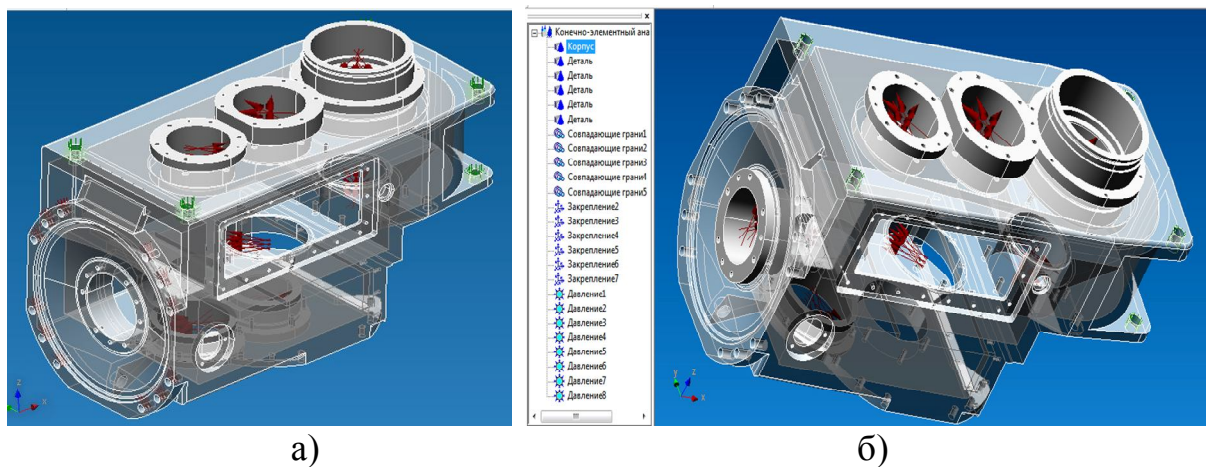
Расчетная модель: а) корпус цилиндрического редуктора, б) корпус коническо-цилиндрического редуктора
